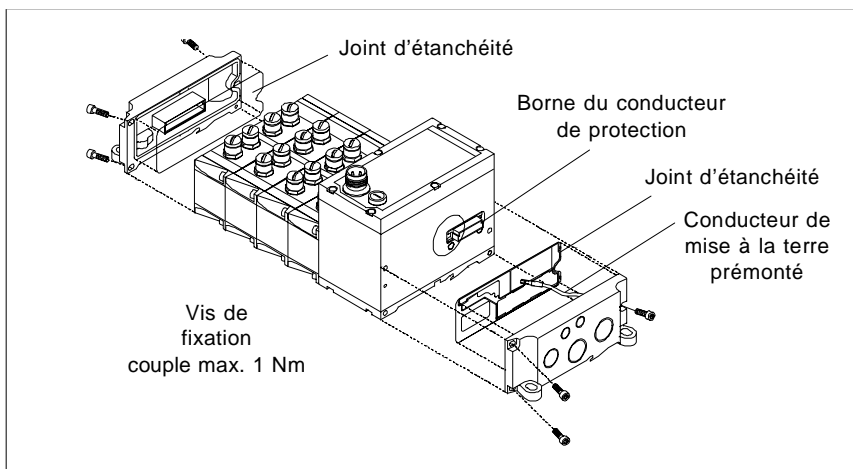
/2 : Montage des plaques d'extrémités (exemple type 03)
